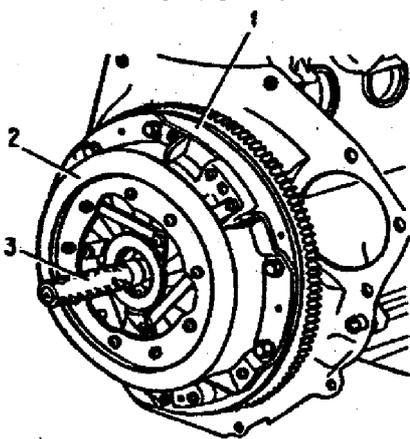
Centralização do disco da embreagem: 1 - volante; 2 - conjunto da embreagem; 3 - mandril A.70081.
